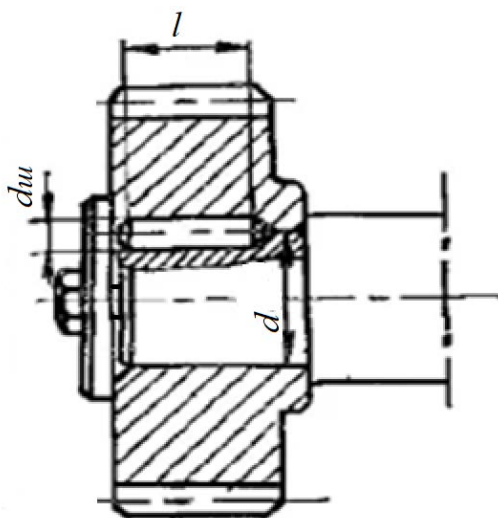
Соединение шестерни с валом цилиндрической шпонкой
